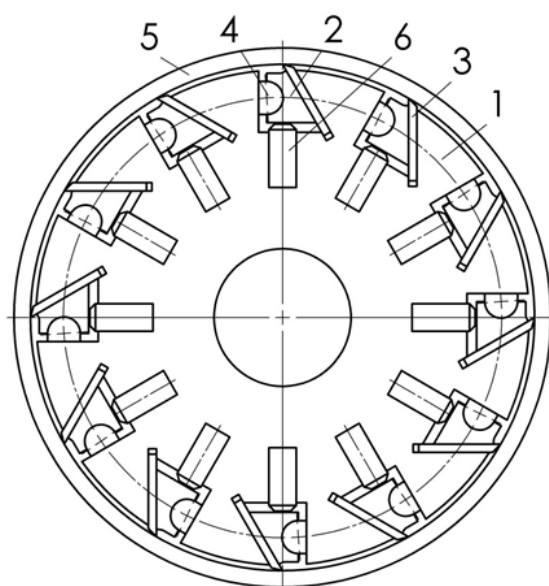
Багатозуба фреза з самовстановними ножами, котрі базуються по фланцях: 1 – корпус фрези; 2 – клиновий стружколамач; 3 – ніж; 4 – проміжна сферична планка; 5 – фланець; 6 – планка
